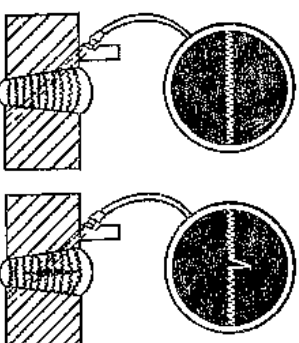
Схема ультразвукового метода контроля сварных соединений:
